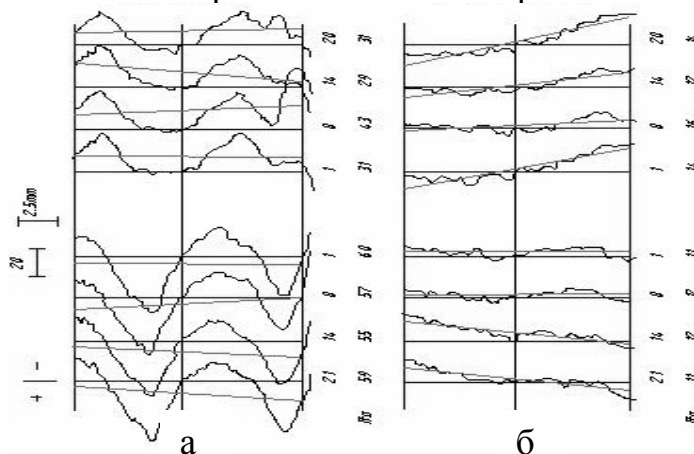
Эвольвентограмма профиля зубчатых колес нарезанных: стандартною а) фрезой предложенной конструкции б).
